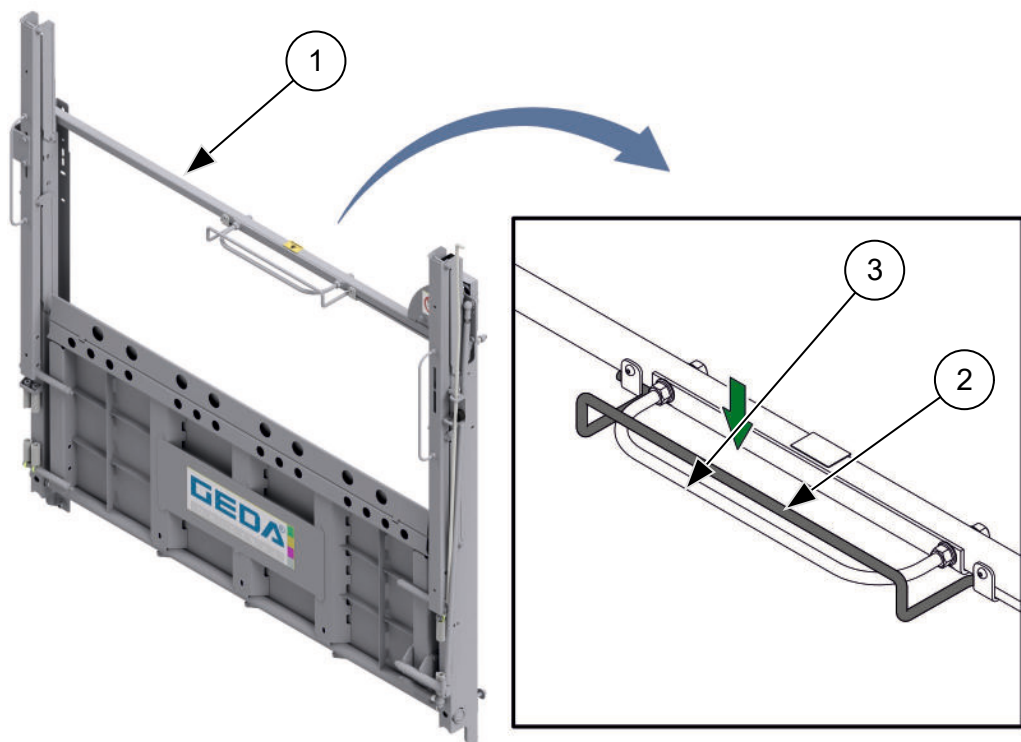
Schranke mit mechanischer Verriegelung öffnen
